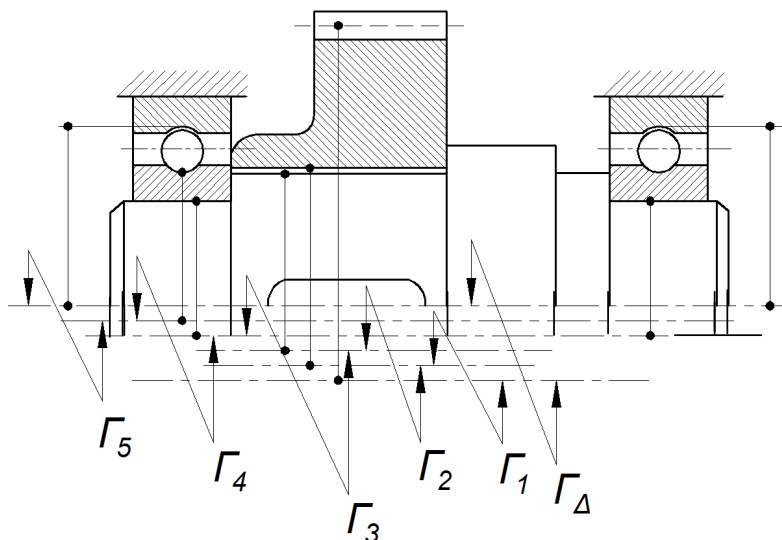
Схема размерной цепи, описывающей формирование несоосности делительного цилиндра зубчатого колеса с его рабочей осью (радиального биения)
